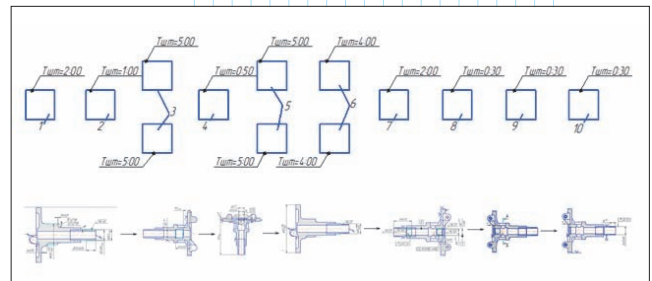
Планировка участка с эскизами детали: 1 – токарно-многолезцовый полуавтомат 1Н713; 2 – токарно-револьверный 1К341; 3 – агрегатный 3ХА-7531; 4 – круглошлифовальный станок 3А151; 5 – алмазно-расточной “SAS” 2ADAR; 6 – агрегатно-сверлильный ХА-13673; 7 – вертикально-сверлильный 2А125; 8 – верстак; 9 – моечная машина; 10 – стол контрольный
